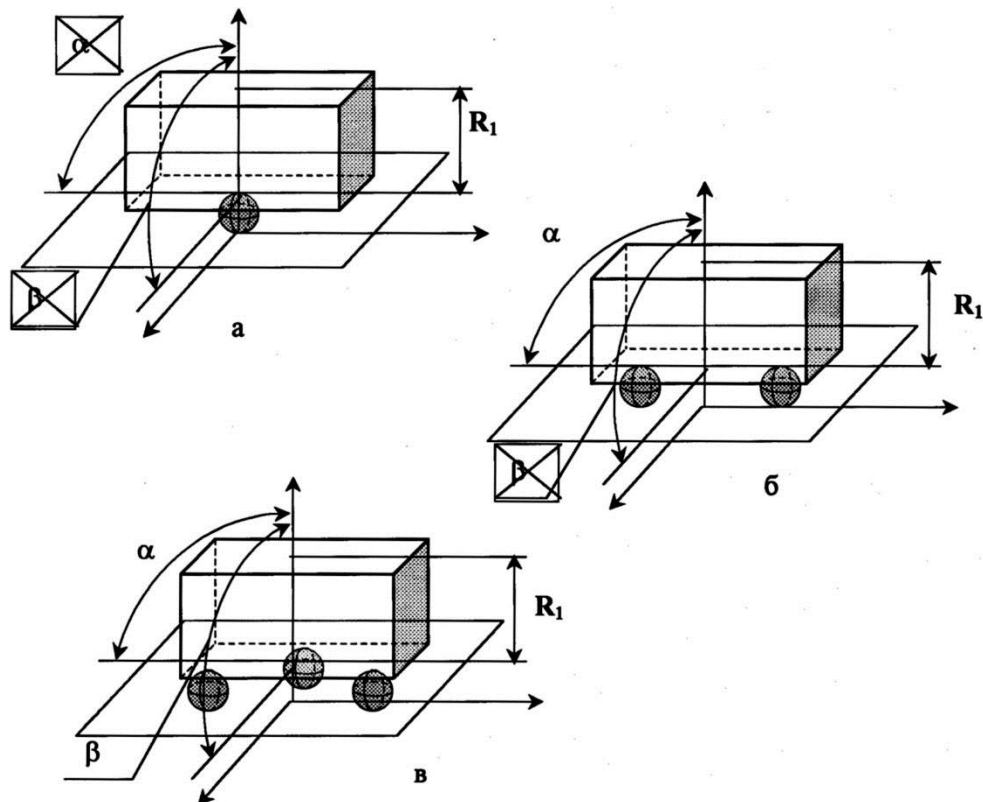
Модель установки заготовки плоской базовой поверхностью [14]:
